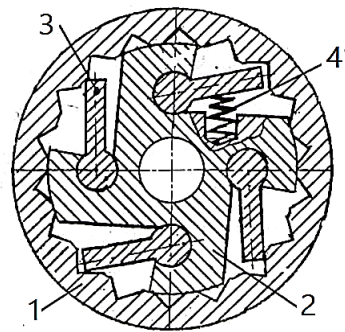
Поворотный механизм с четырьмя собачками в корпусе: 1 — храповое кольцо; 2 — храповой стержень; 3 — собачка; 4 — пружина.
